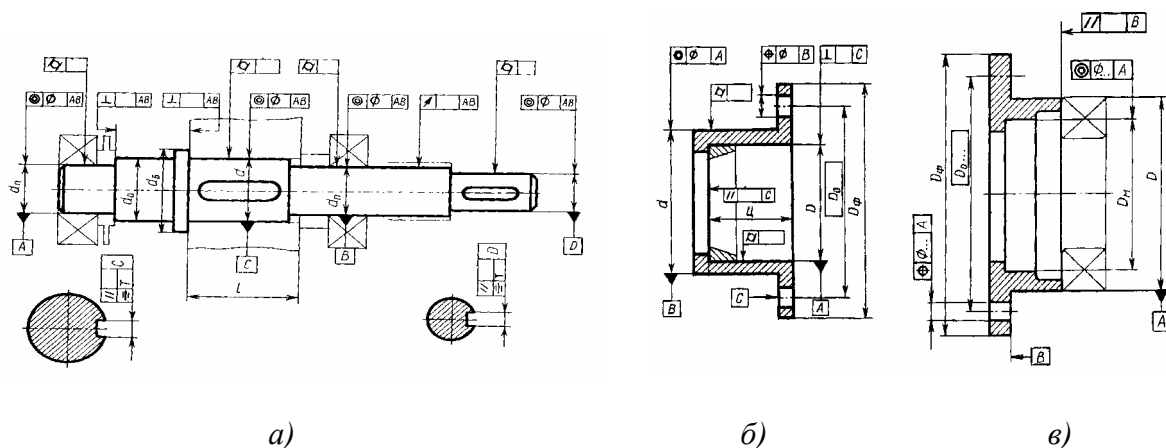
Допуски формы и расположения для некоторых деталей:
